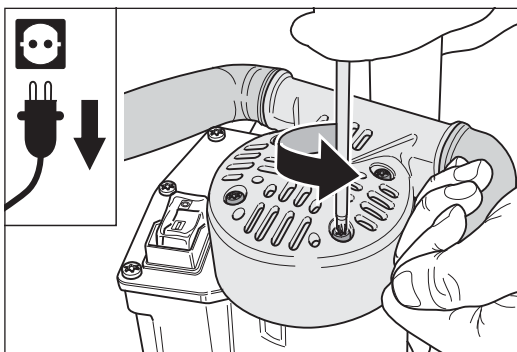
Die vier Befestigungsschrauben des Griffstücks entfernen.
